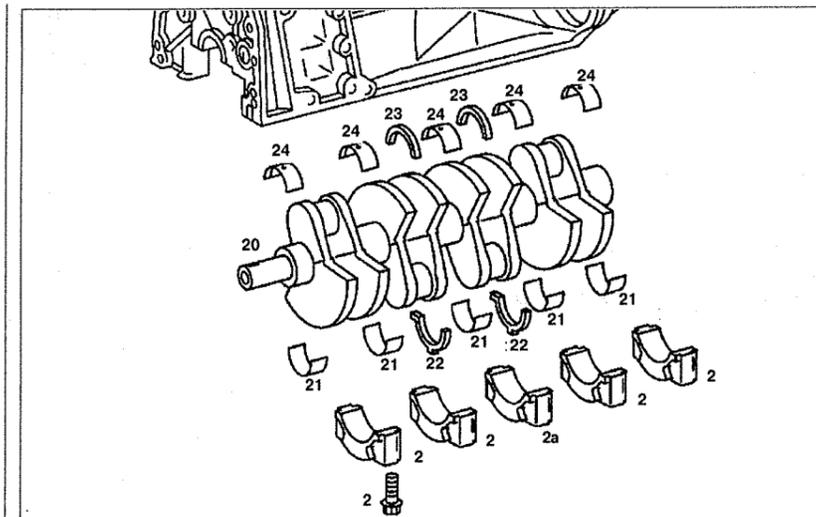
Коленчатый вал: 2. Крышка коренного подшипника, 2a. Установочная крышка, 3. Болт, 20. Коленчатый вал, 21. Нижний вкладыш, 22. Нижняя упорная прокладка, 23. Верхняя упорная прокладка, 24. Верхний вкладыш (с масляным каналом).
